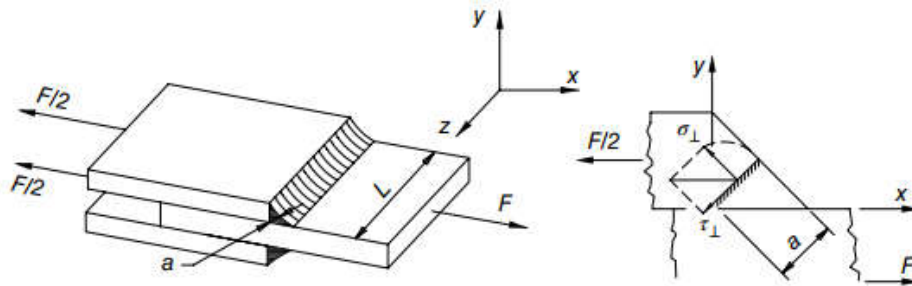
Plaques assemblées par des cordons de soudure transversaux
